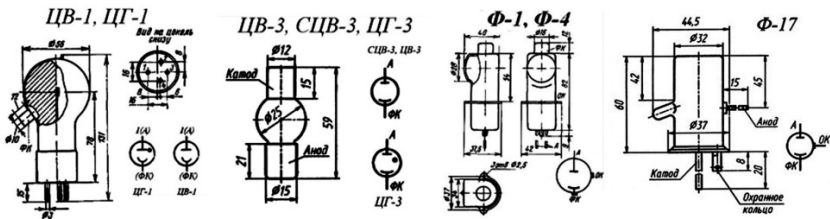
Внешний вид и габаритные размеры фотоэлементов
